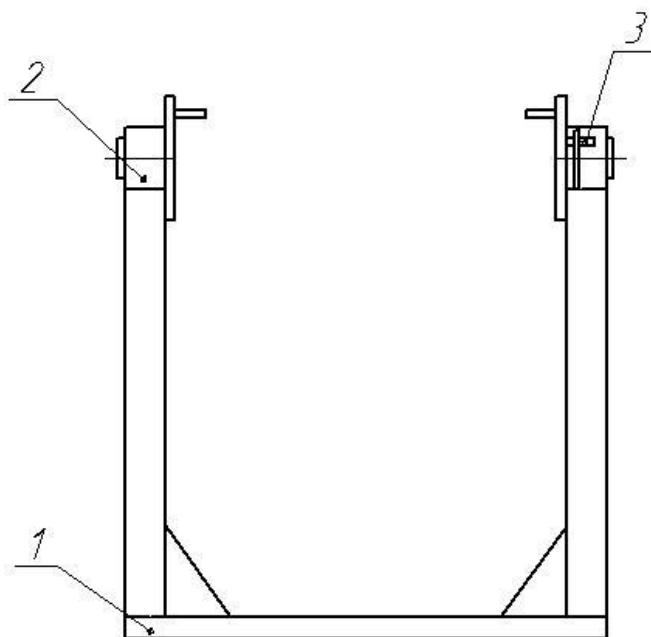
Схема стенда для разборки и сборки редукторов, модель 17-13
